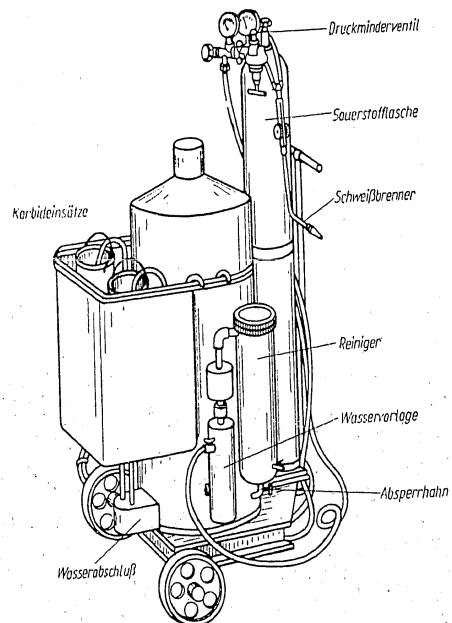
Fahrbare Azetylenentwickler-Schweißanlage
